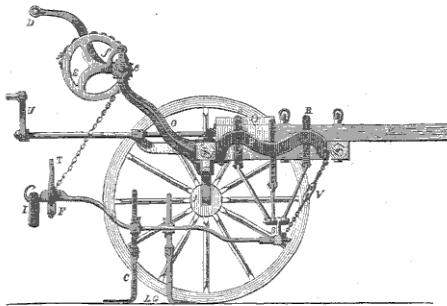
Coupe longitudinale de la bineuse Garrett.
